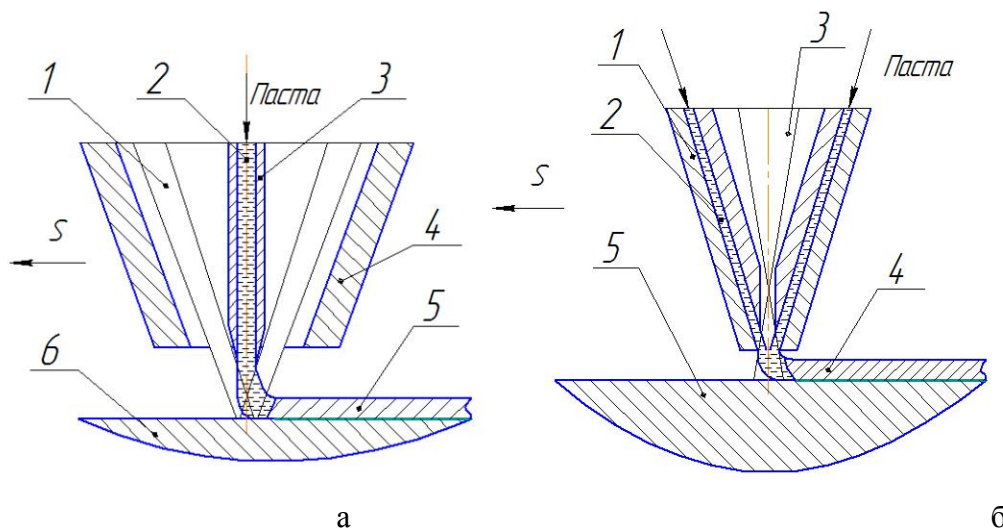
Схеми лазерної поверхневої обробки з кільцевою (а) та круговою (б) формою перерізу зфокусованного променя при співвісній подачі пастоподібної суміші: 1– сопло, 2- паста, 3- лазерний пучок, 4- наплавлений матеріал, 5- деталь
